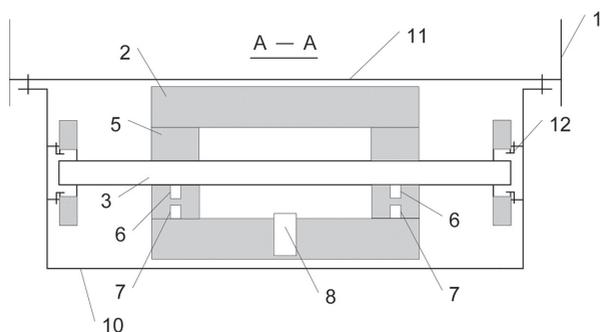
Разрез устройства: 1 – транспортное средство; 2 – противовес; 3 – направляющие штанги; 5 – поршни; 6 – левый фиксатор; 7 – правый фиксатор; 8 – пиропатрон; 10 – корпус; 11 – днище транспортного средства; 12 – амортизаторы
